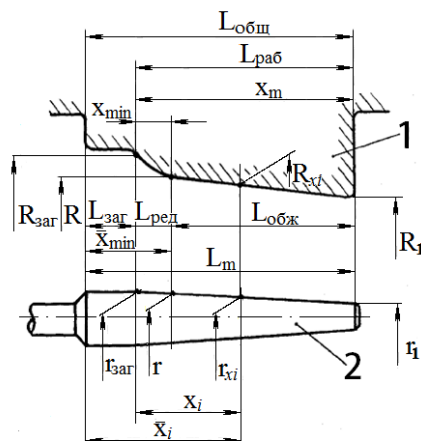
Схема калибровки прокатного инструмента станков ХПТК:
